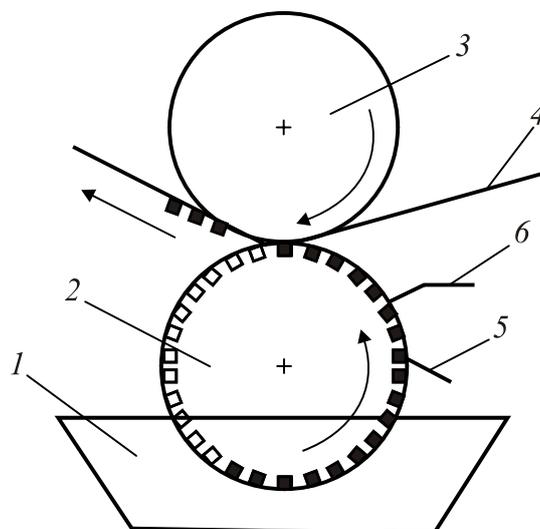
Схема печатного аппарата машины глубокой печати:
